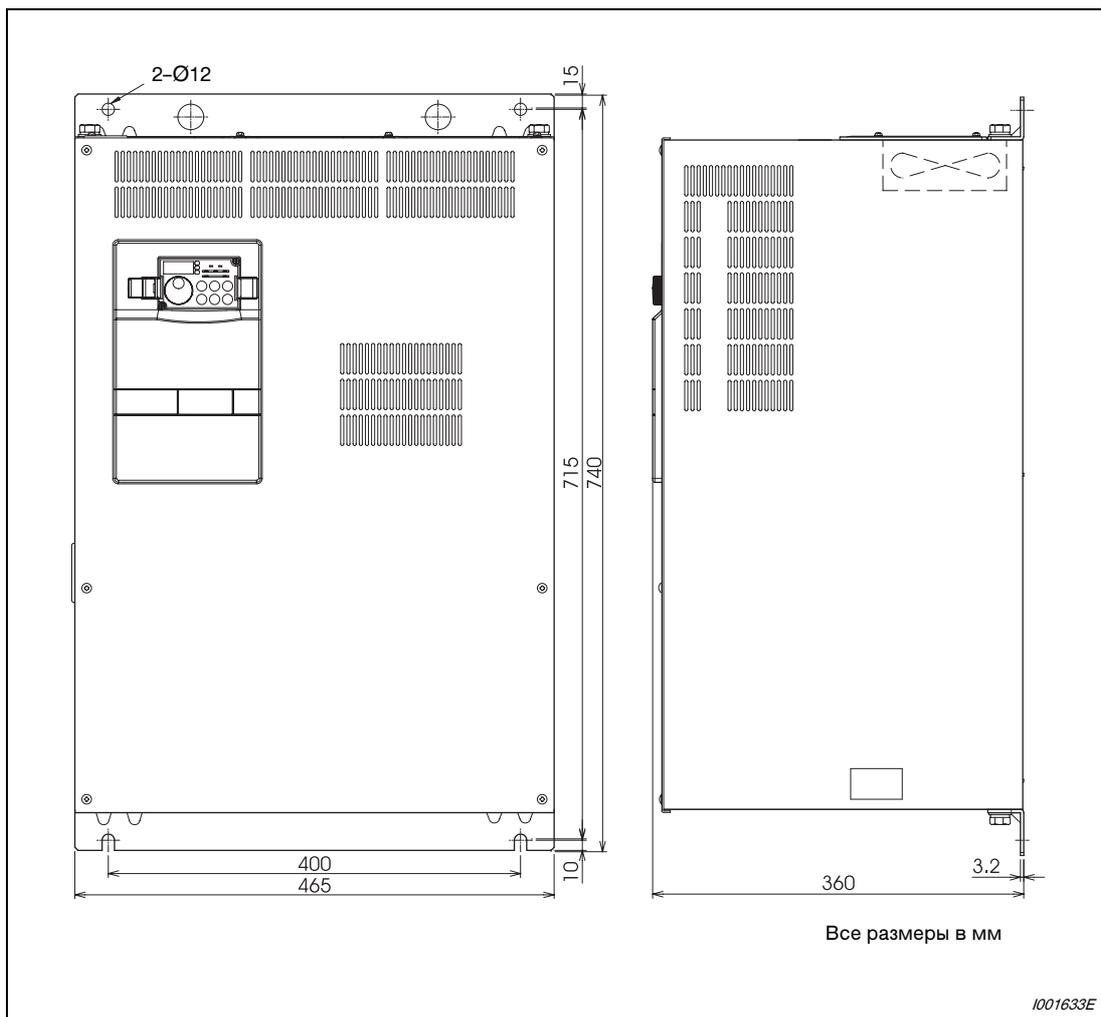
Размеры FR-A 740-03250 и FR-A 740-03610
